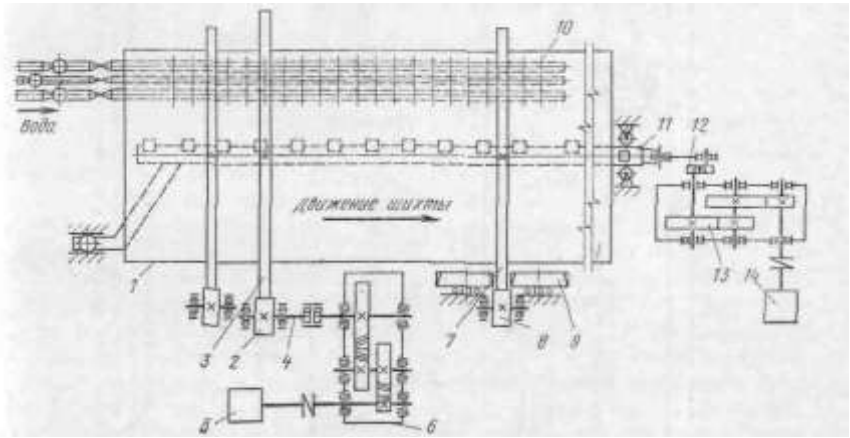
Кинематическая сема привода барабанного смесителя
